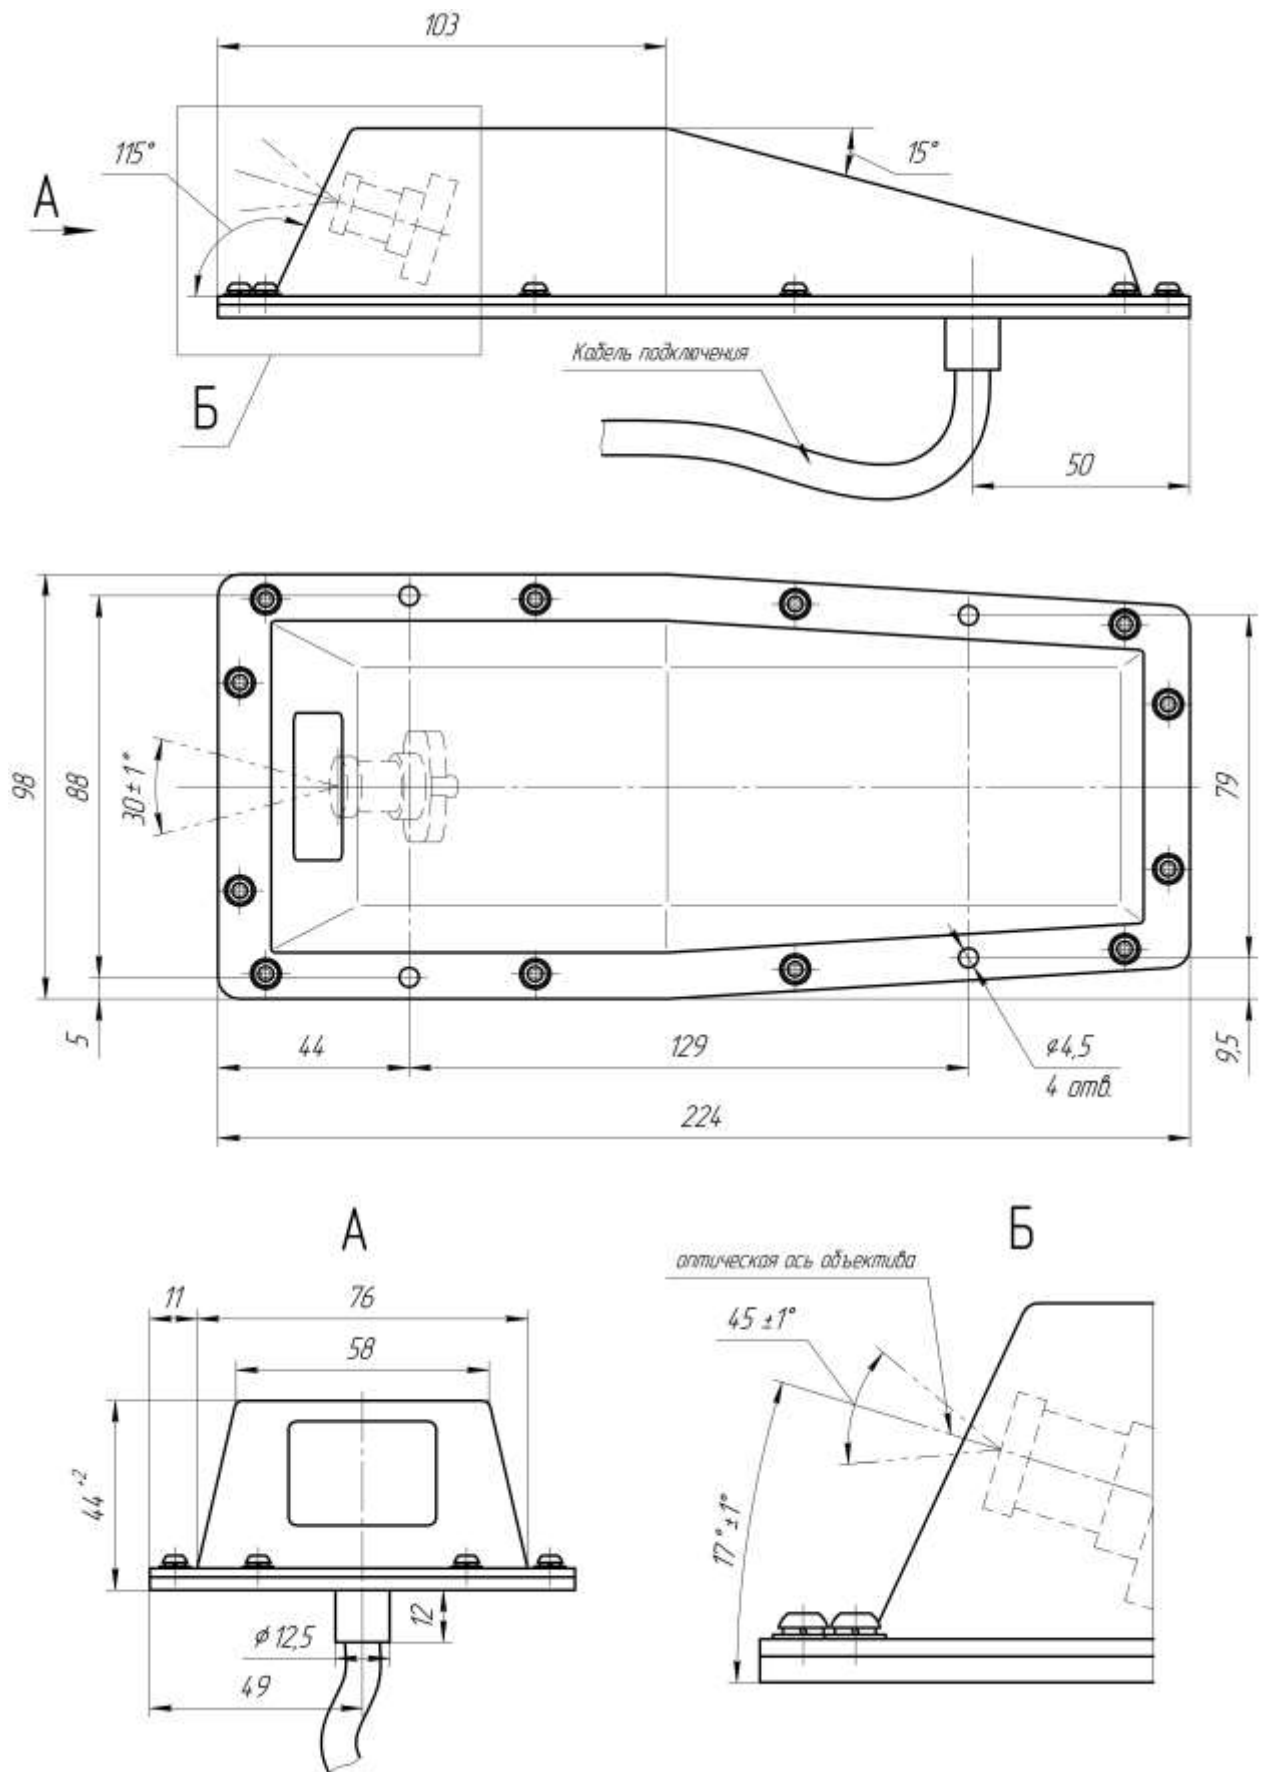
Габаритные и установочные размеры камеры видеонаблюдения
